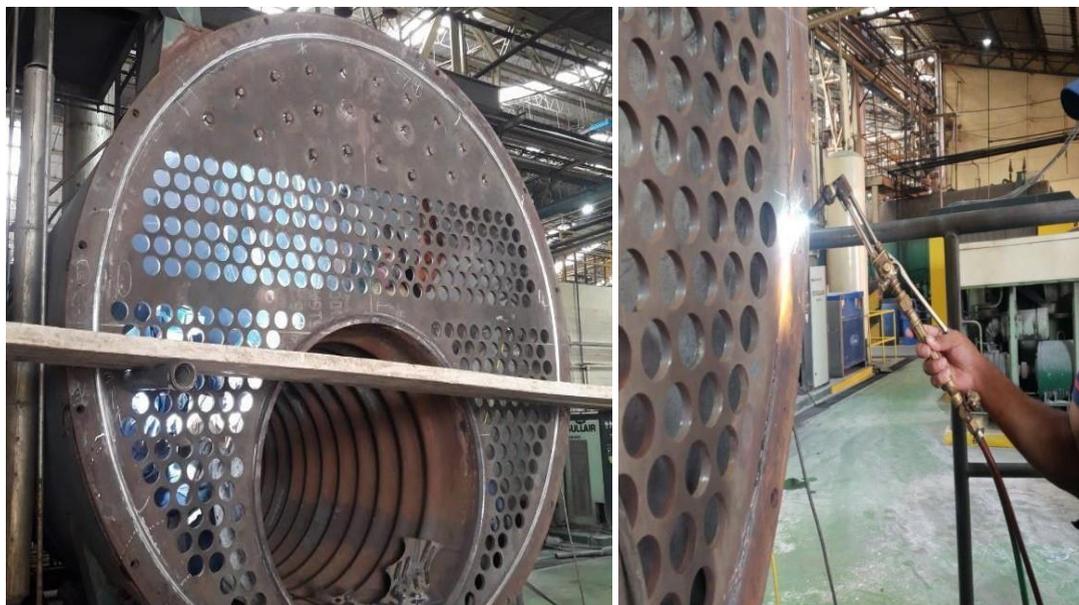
Soldadura exterior de junta entre anillo del cuerpo y espejo nuevo.
